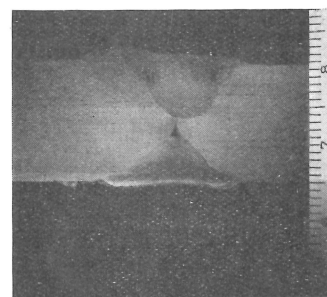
Coupe transversale dans la soudure [représentée figure 6a.
